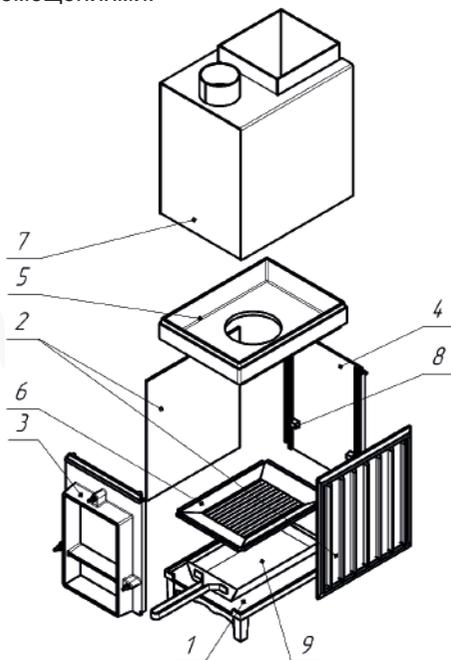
Схема сборки топочного агрегата печи Сударушка Руса-Семейная, Сударушка Семейная.
